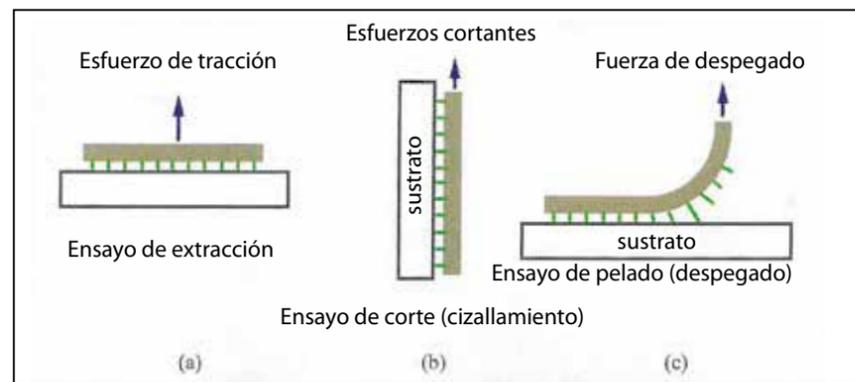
Tres tipos de prueba comunes para medir la adhesión: extracción, corte y pelado.
